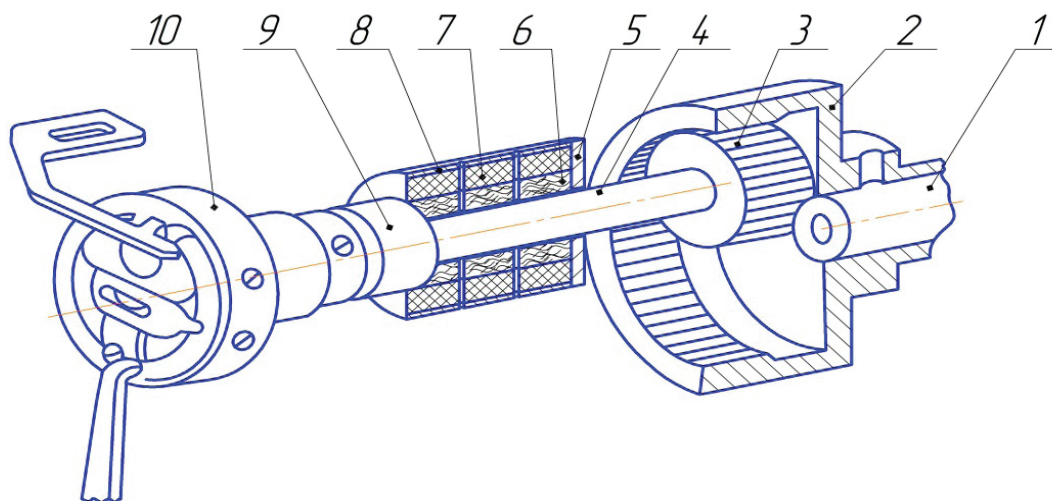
Конструктивная схема механизма челнока и отводчика шпулдержателя: 1 – нижний вал; 2,3 – зубчатое колесо и шестерня; 4 – челночный вал; 5 – опорная шайба; 6 – войлок; 7 – шкурка; 8 – наружная втулка; 9 – челночная втулка; 10 – челночное устройство
